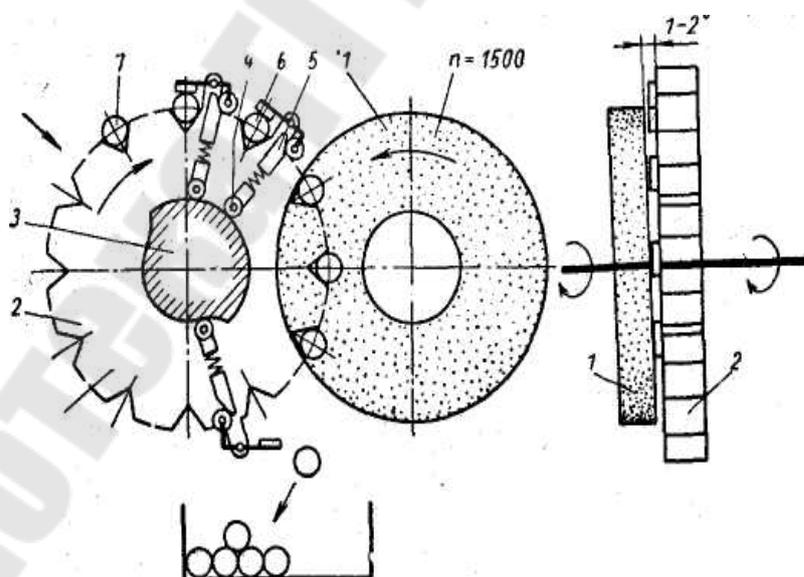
Принципиальная схема полуавтомата для зачистки торцов мелких отливок: 1- шлифовальный круг; 2- питающий диск; 3- неподвижный кулак; 4- ролик; 5- клин; 6- зажимной рычаг; 7- зачищаемая отливка
